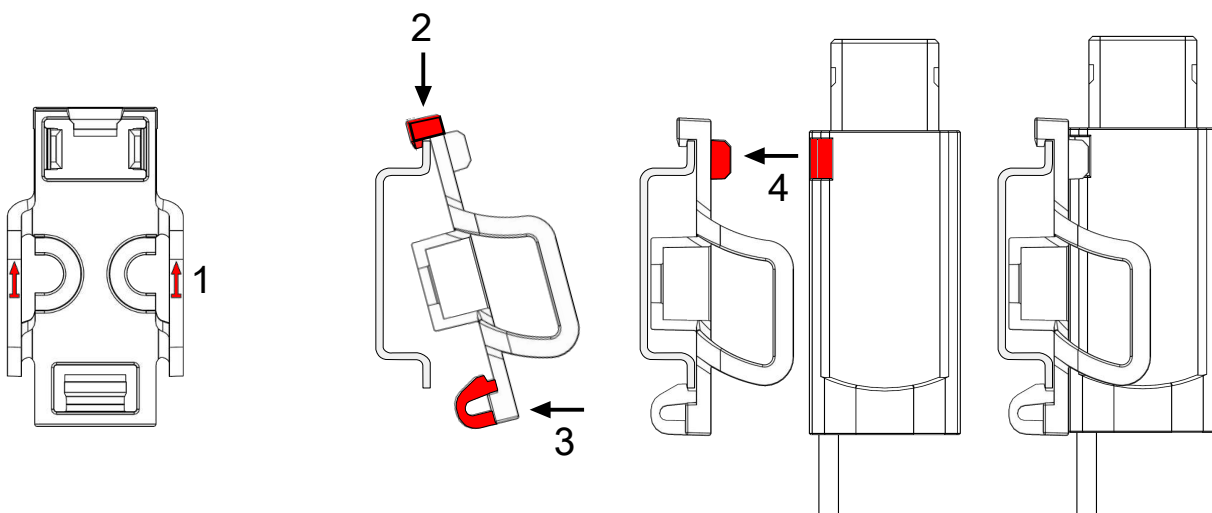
Befestigung der SCL/SVL-Wandler auf der Tragschiene mit Hilfe der Schnappbefestigung ZB8201-0900
